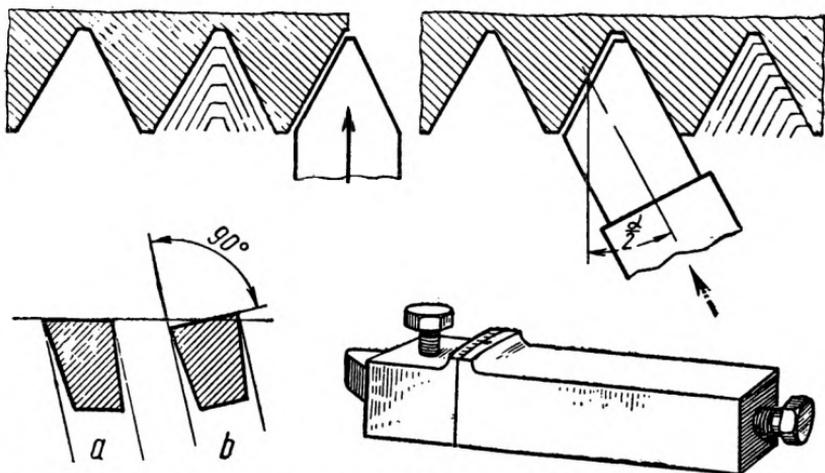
Способы нарезания треугольной резьбы и резцовая державка.
